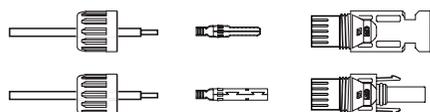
Desmontaje del conector de la tuerca de sombrerete
